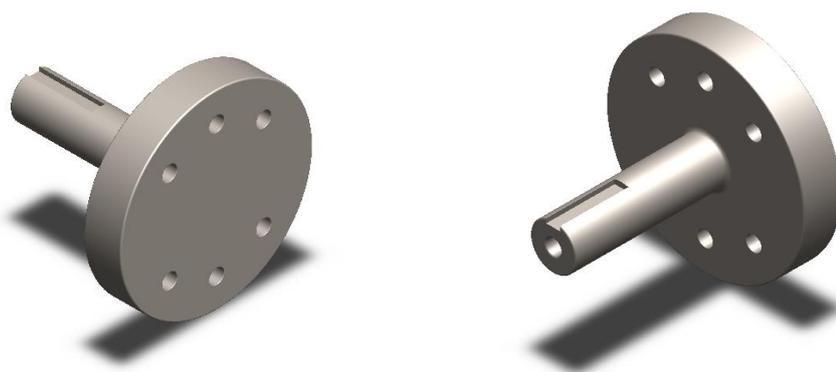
Vistas isométrica acople motor. Fuente: Captura SolidWorks
